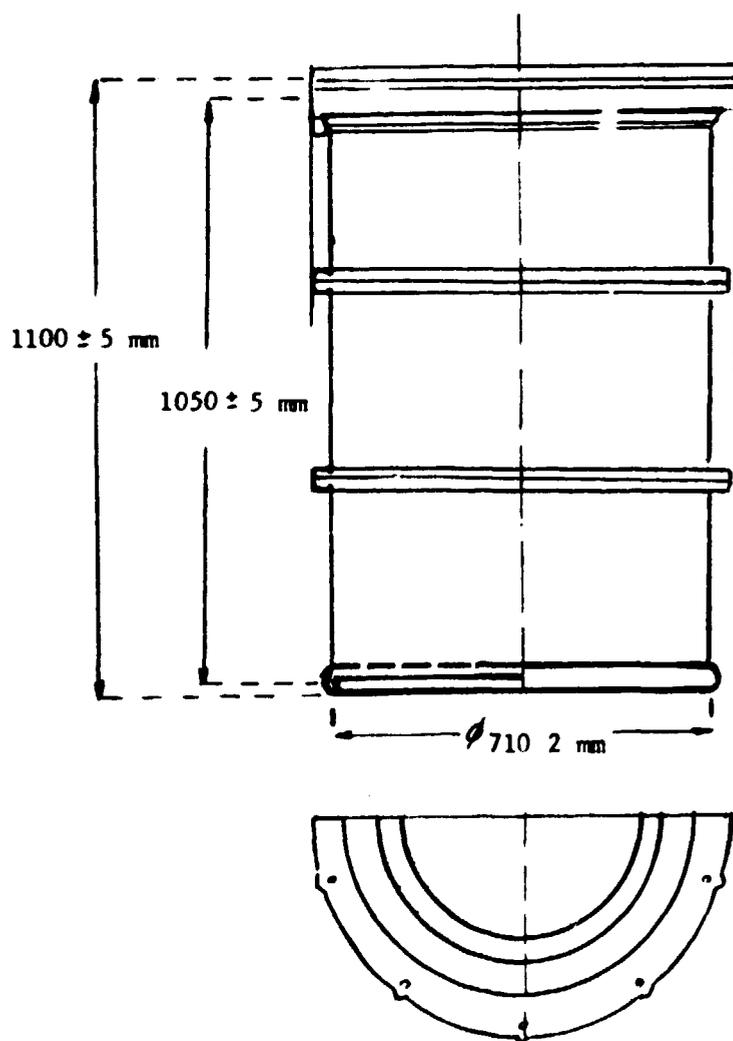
Tambor em aço de 400 L com tampa parafusada.
